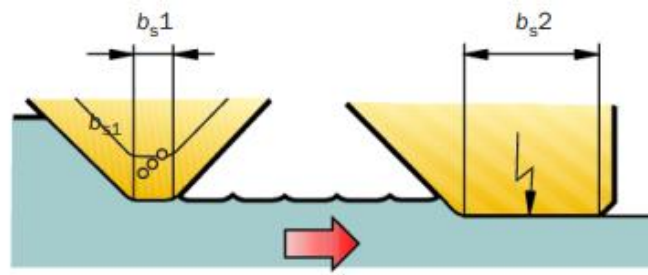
Пластини з Wiper геометрією для зачистки поверхні
